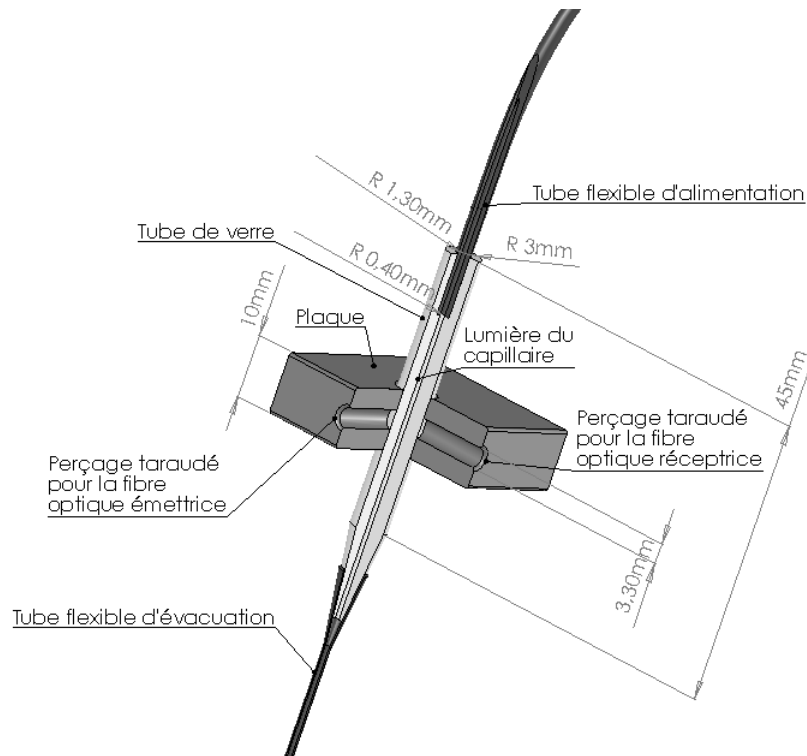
Vue en coupe du montage d'un capteur à fibre optique
